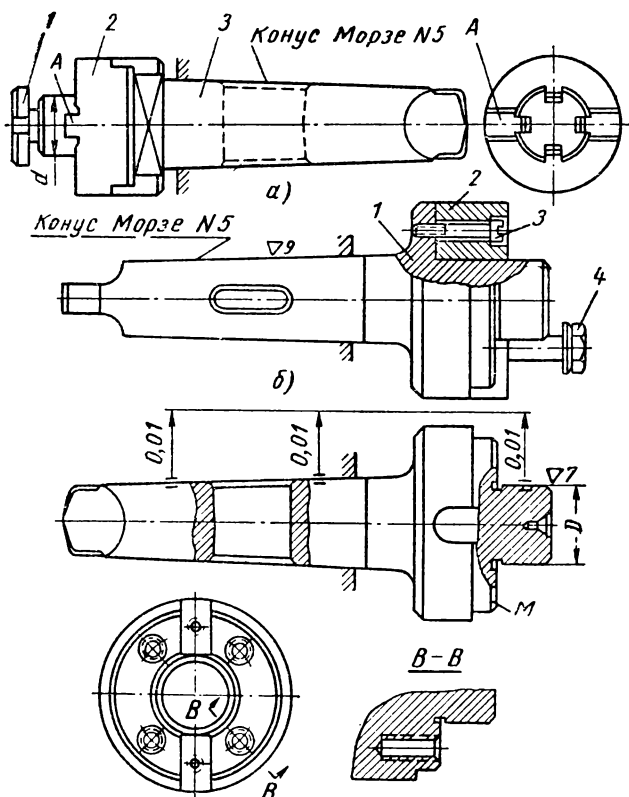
Оправки для крепления фрез: а — для фрез диаметром от 40 до 110 мм; б — для фрез диаметром от 150 до 400 мм
